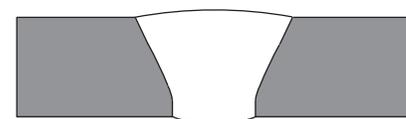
Exemple de soudure incorrecte n° 2
